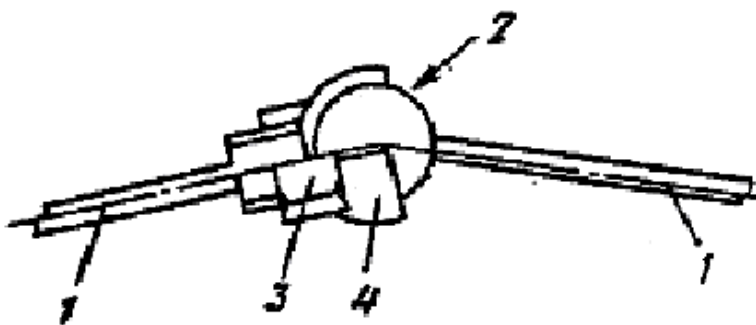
Устройство первого варианта нагрузочного механизма шарнира (1 - звенья, 2 - сфера, 3 - прижимная гайка, 4 - цанговый зажим)
